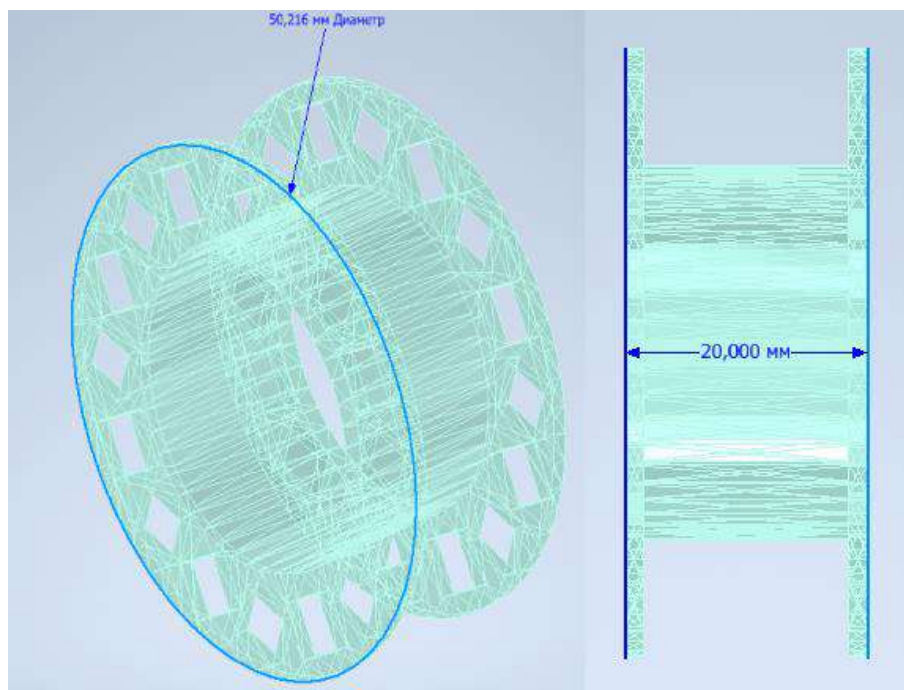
3D-модель каркаса магнитной сборки (вид со стороны и сбоку)
